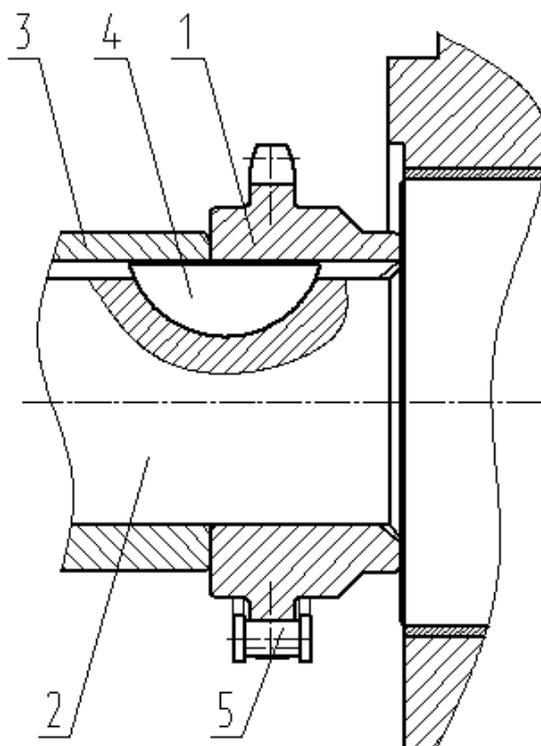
Фрагмент коленчатого вала в сборе.
